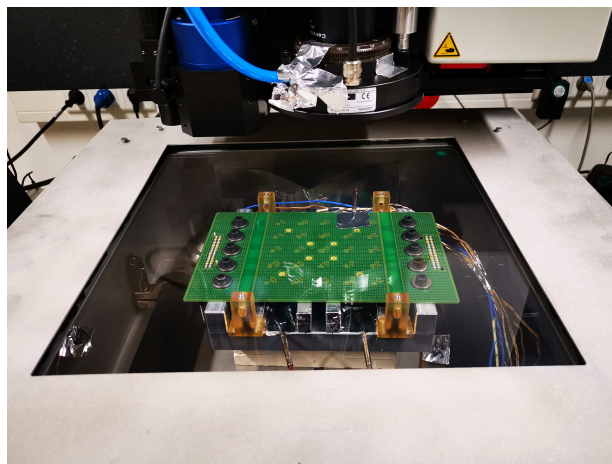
Testboard für QFN-Packages on board unter thermischer Belastung in der BNT-HCC
